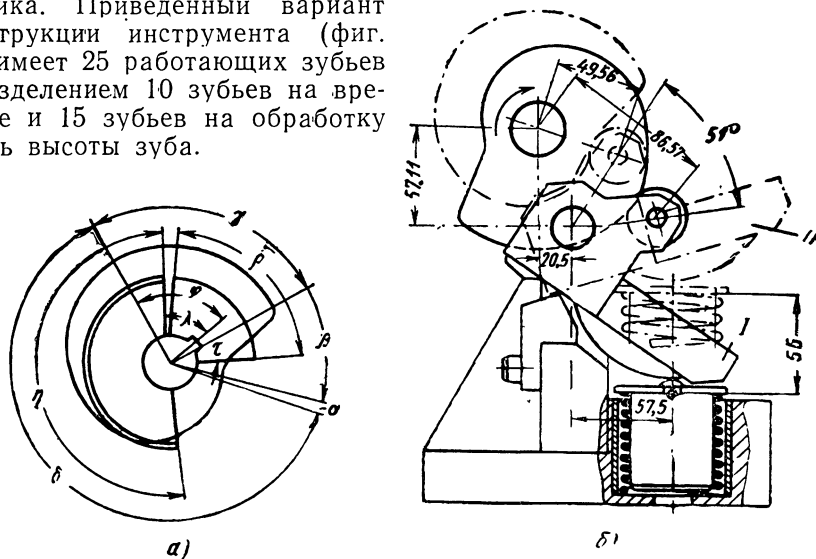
Комбинированный инструмент для зубозакругления зубчатых колес $t = 3$ мм по направлению от впадины зуба (вариант первый).
